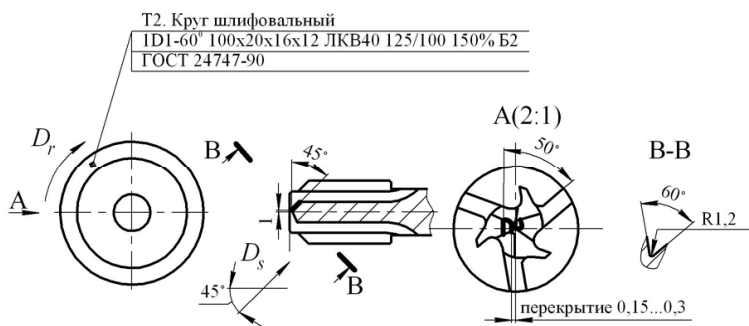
Прорезка канавки между торцовыми зубьями на шестом переходе
